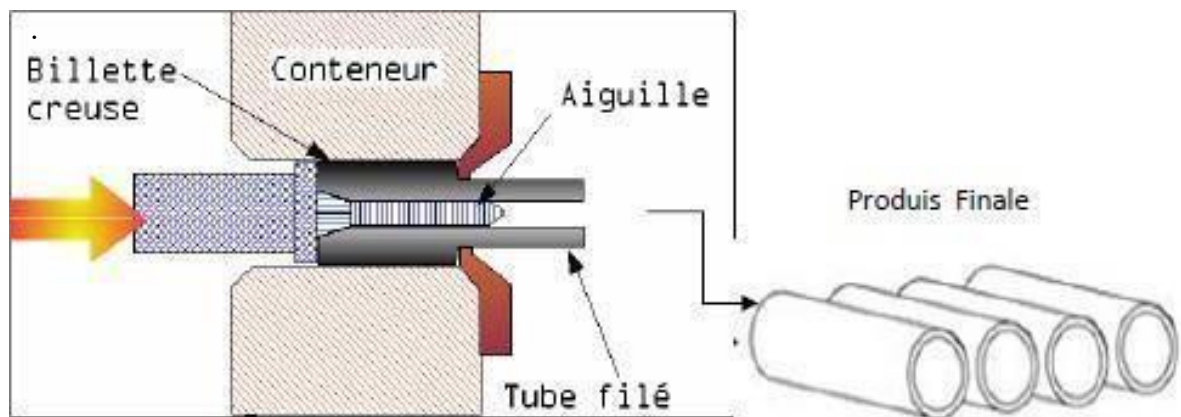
Fabrication des tubes sans soudures [32].
